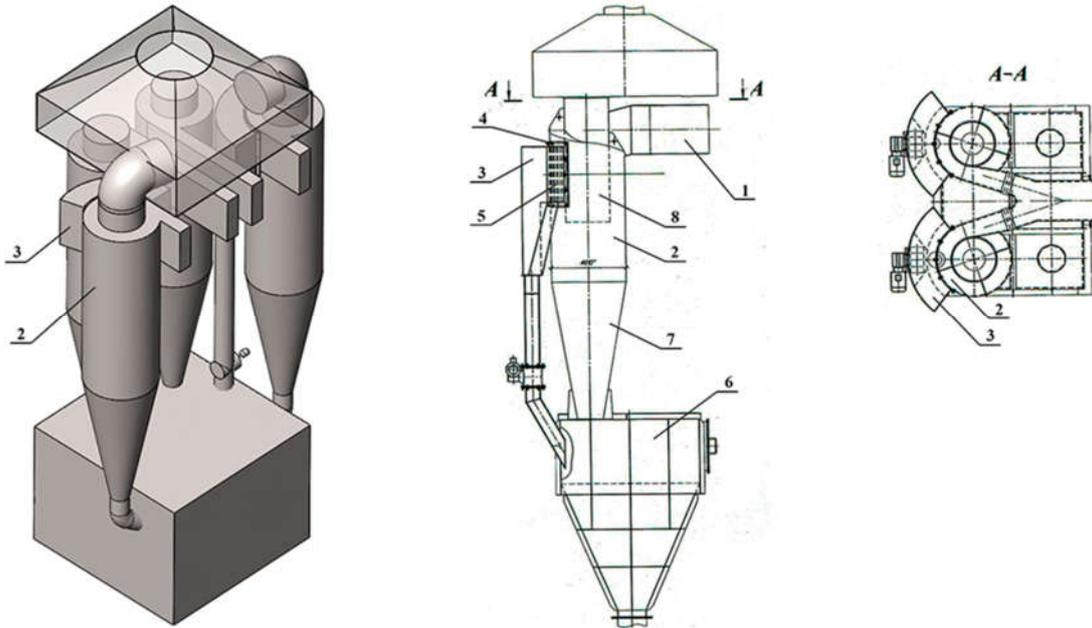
Циклон с водяной пленкой ЦВП: 1- корпус; 2- выходной патрубок; 3- улитка; 4- коллектор; 5- конусный патрубок (гидрозатвор); 6- входной патрубок
